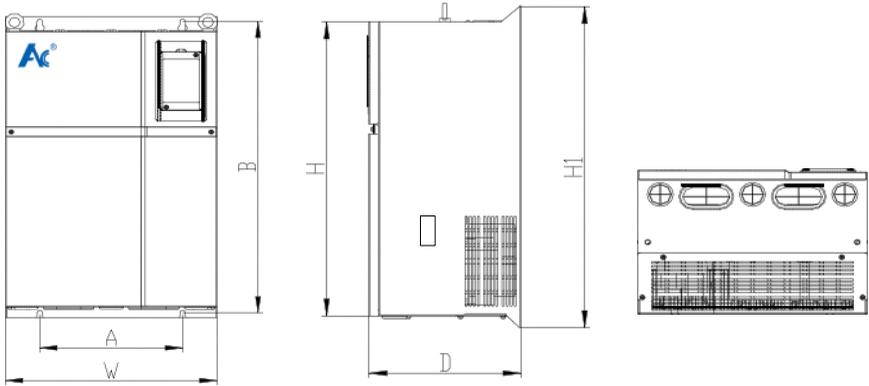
AC900 系列钣金结构外型尺寸及安装尺寸示意图
